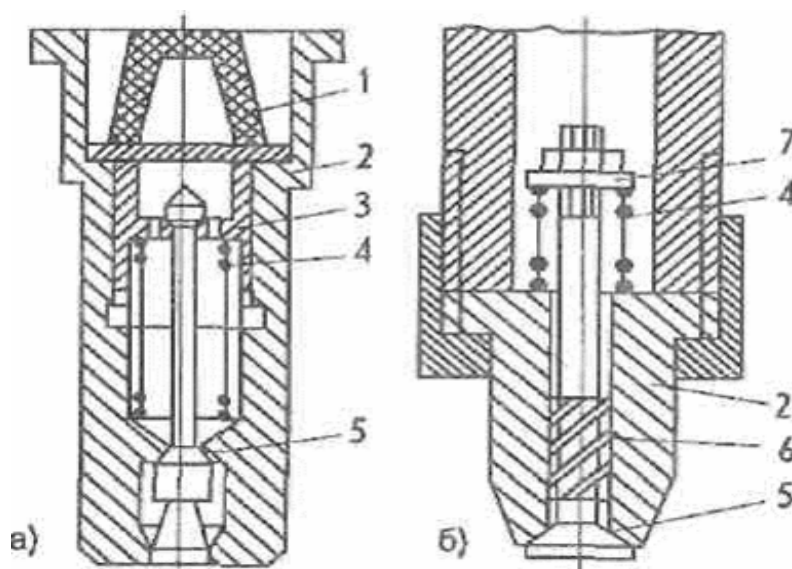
Распылители клапанных форсунок: а - с штифтовым клапаном; б - с винтовыми канавками на стержне; 1 - фильтр; 2 - корпус; 3 - подвижная опора; 4 - пружина; 5 - клапан; 6 - стержень; 7 - гайка
